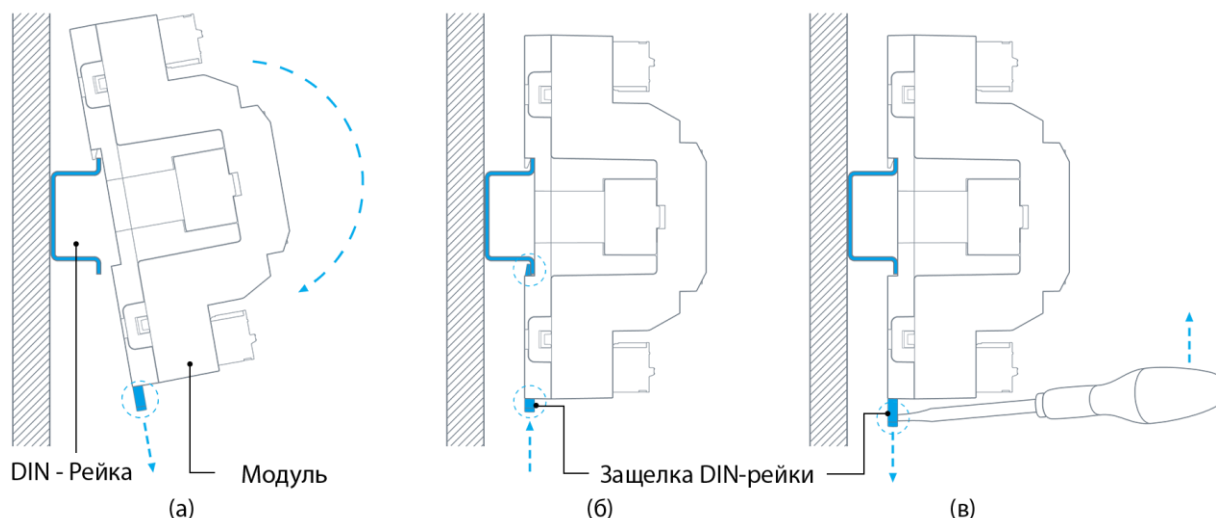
а, б) Монтаж прибора на DIN-рейку в) Демонтаж прибора с DIN-рейки
